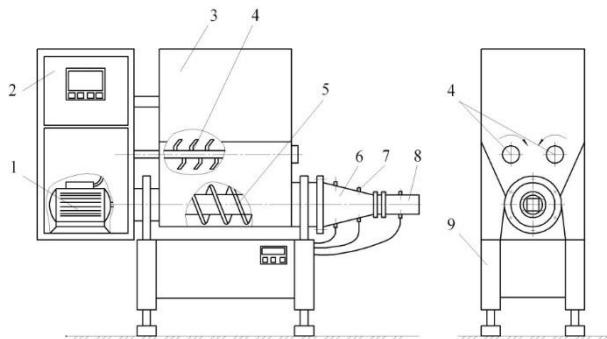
Формовочный автомат фирмы Bouwpraco BPEX4500: 1 – привод; 2 – щит управления; 3 – приемный бункер; 4 – ворошилели; 5 – шнек; 6 – формующий канал; 7 – датчик давления; 8 – мундштук, 9 – рама
